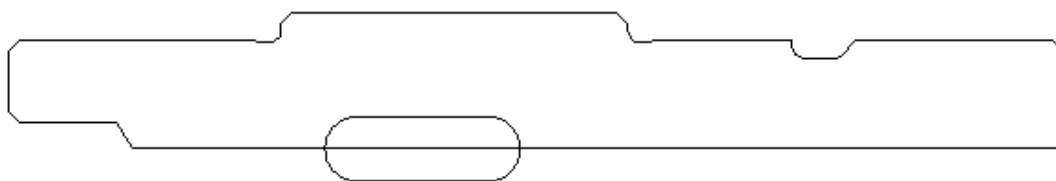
Контур половины вала и шпоночного паза,
